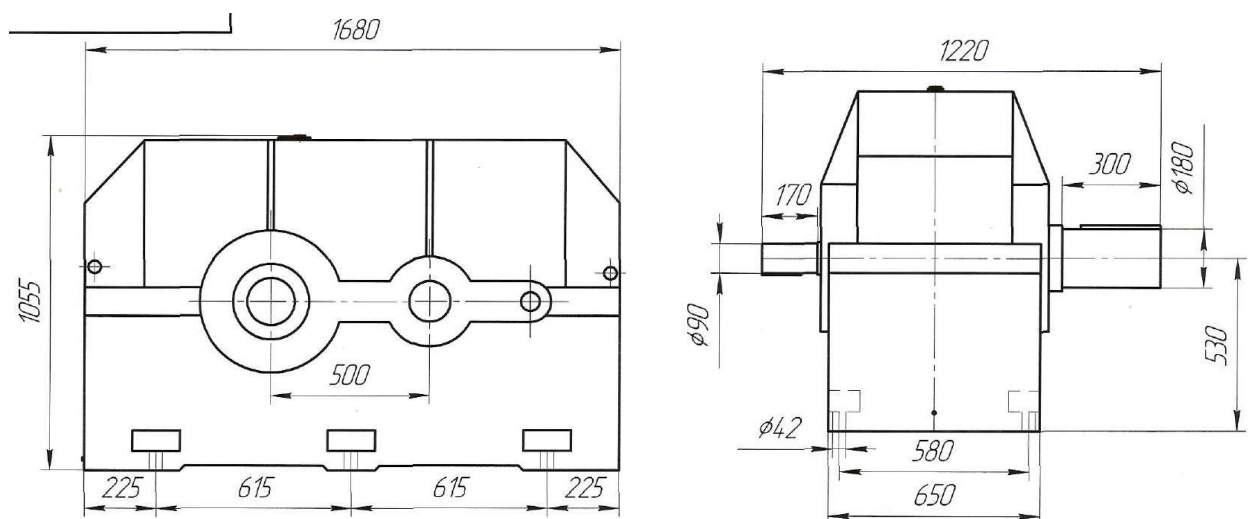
Ескіз редуктора типу Ц2Н-500.
